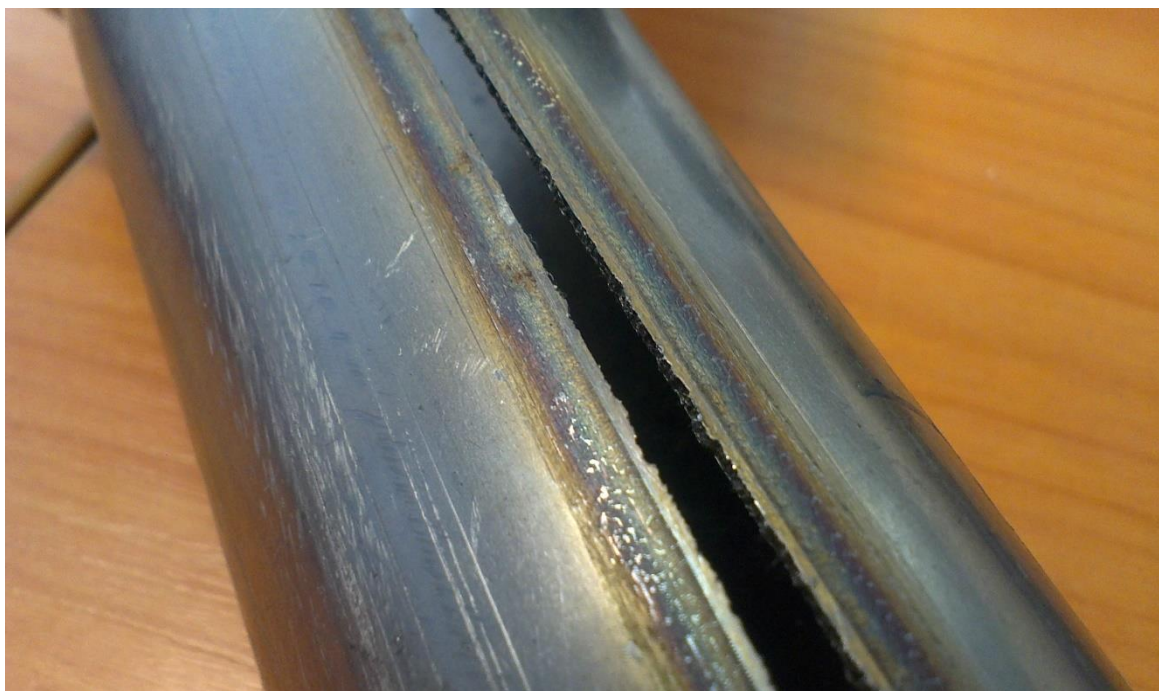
Непровар сварочного шва на электросварной трубе
